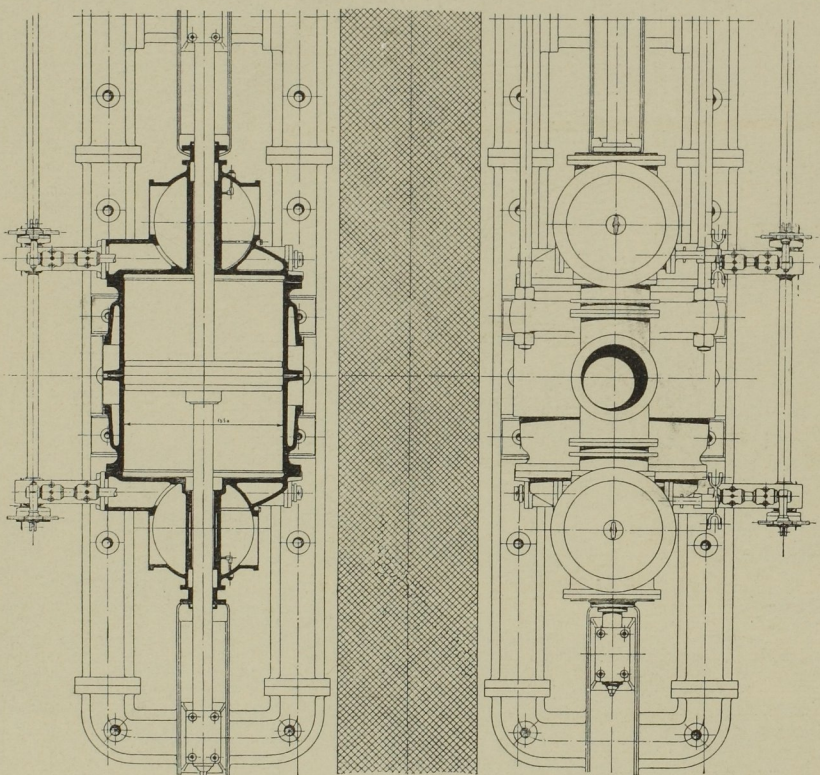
Grundriss und Längsschnitt des Windzylinders. Massst. 1 : 60.
